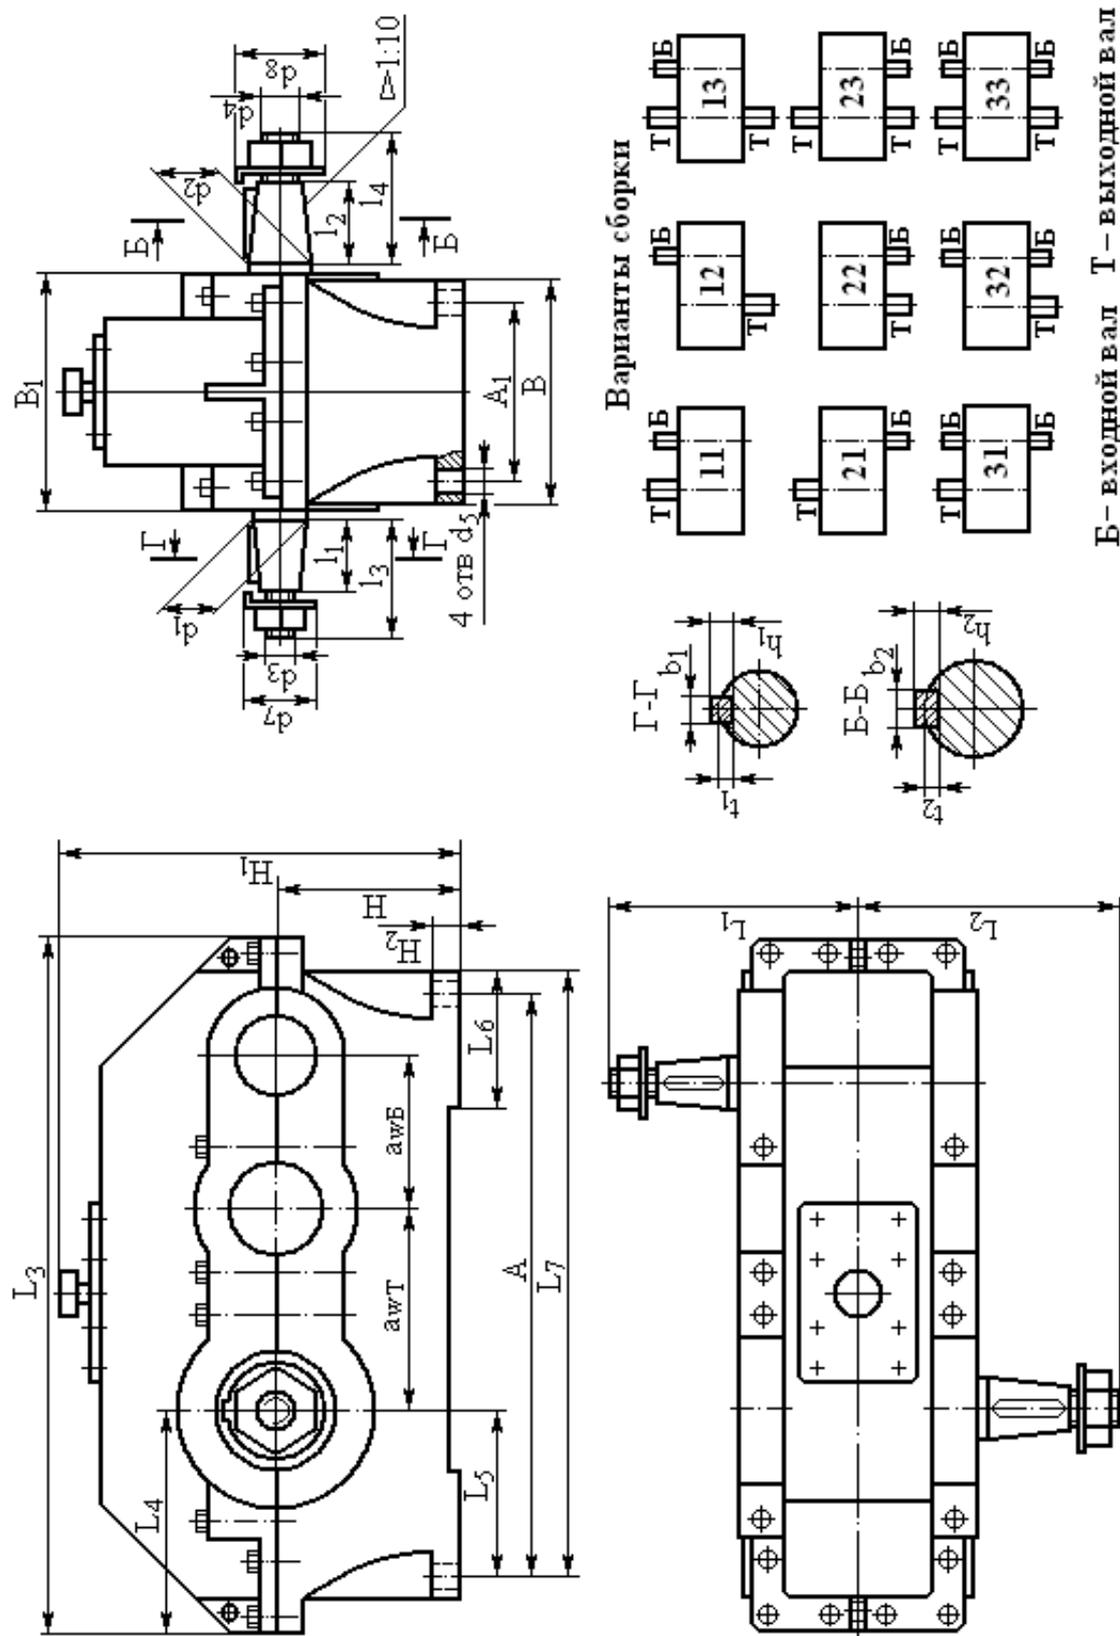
Цилиндрический двухступенчатый редуктор типа Ц2У
